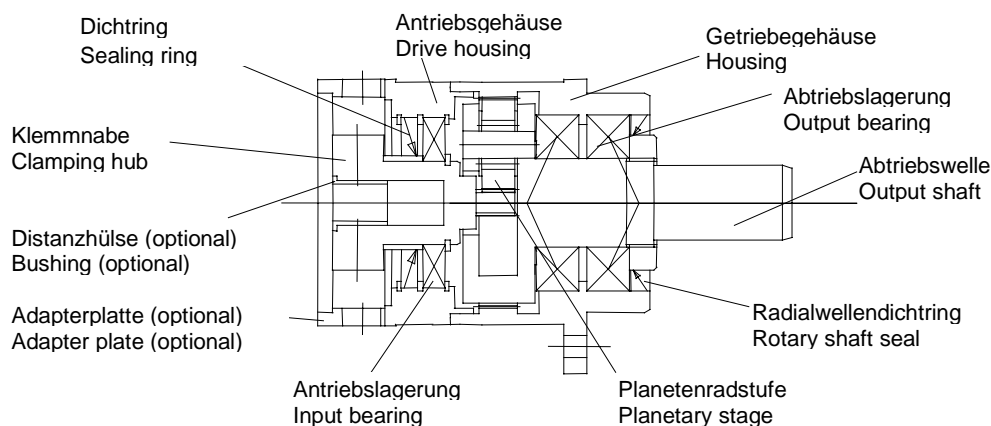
Aufbau der einstufigen Motoranbauversion
